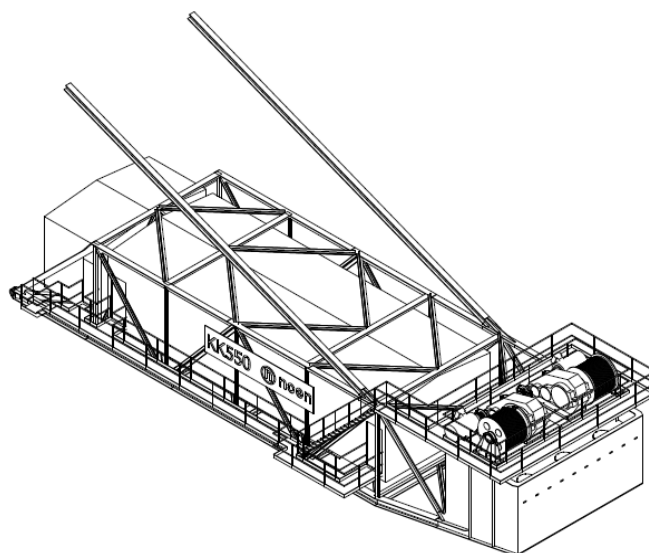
Předávací výložník rýpadla KK 550 [5]
